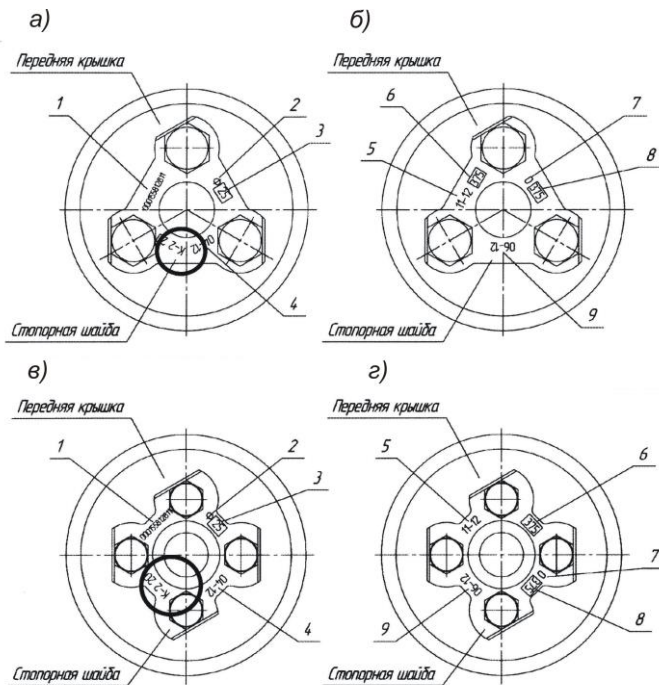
Внешний отличительный признак конических подшипниковых узлов под адаптер:
